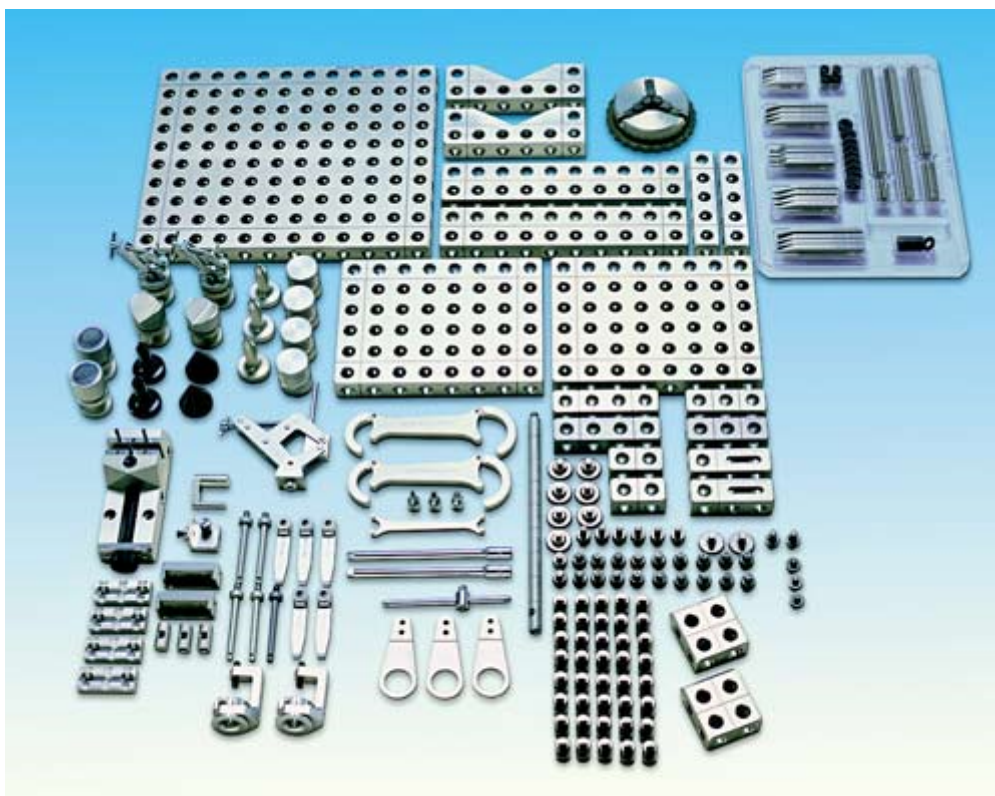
Příklad sestavy hydraulického upínání - ROEMHELD[12]
